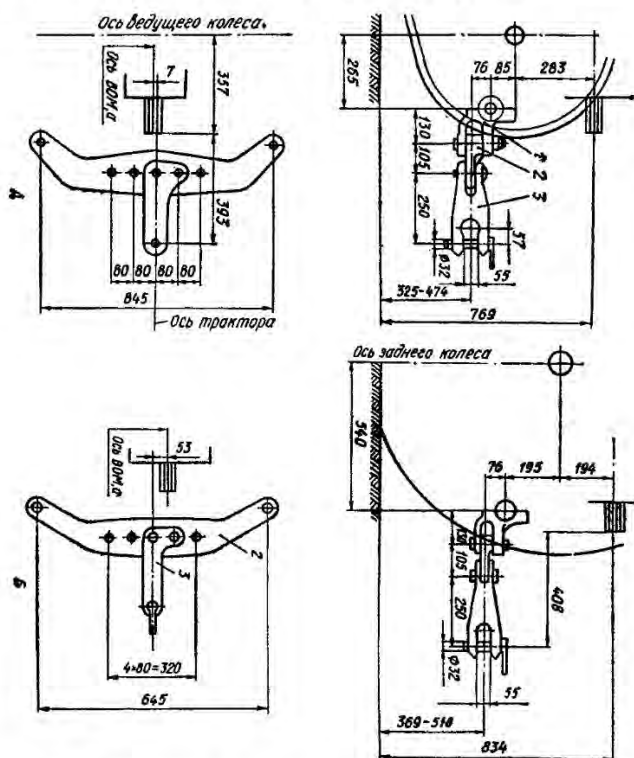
Схема взаимного расположения вала ВОМ и прицепной скобы:
